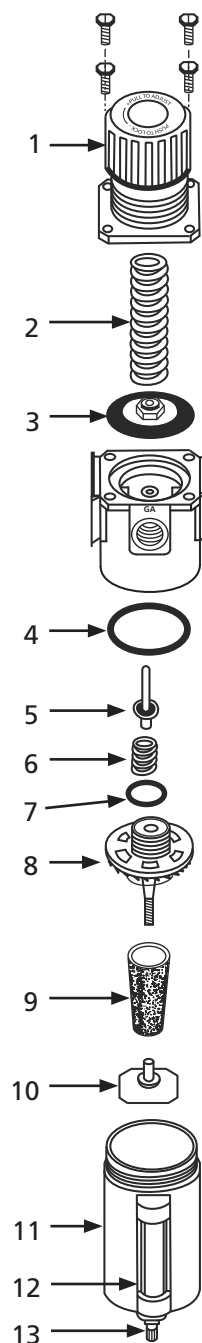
Illustration des pièces détachées pour le filtre/régulateur
